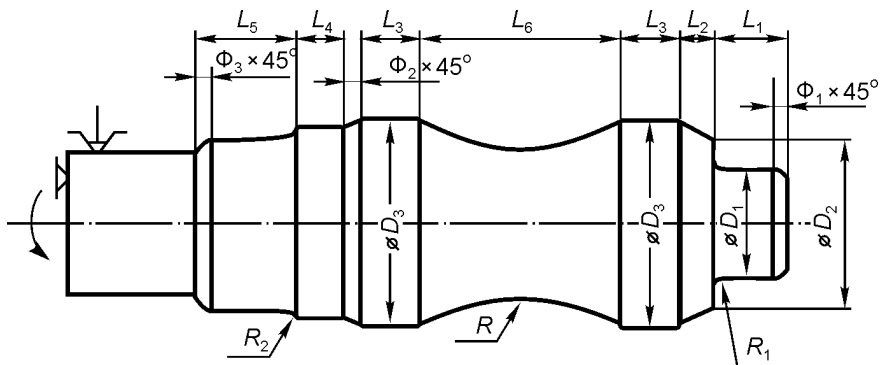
Ескіз деталі до контрольного завдання програмування чистової двоінструментальної обробки валика
